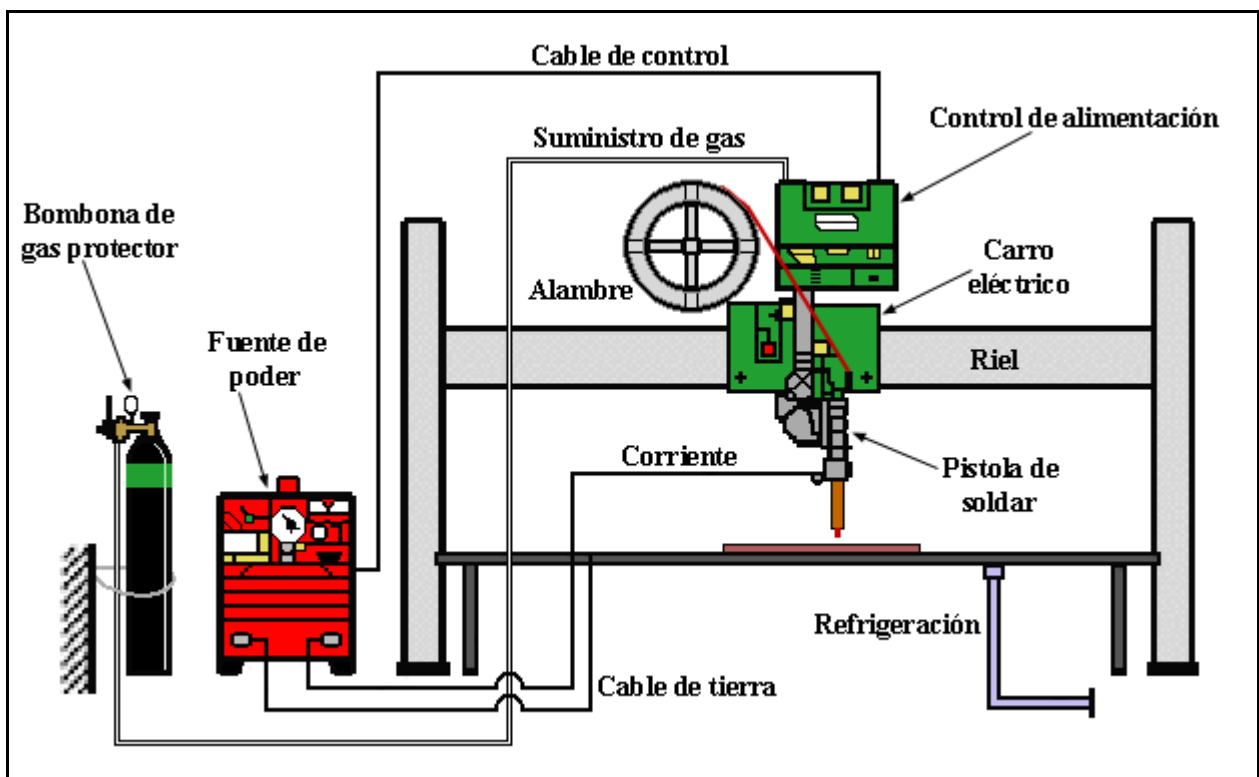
Diagrama esquemático del equipo para soldadura GMAW.
